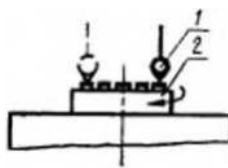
Схема проверки торцового биения рабочей поверхности стола
